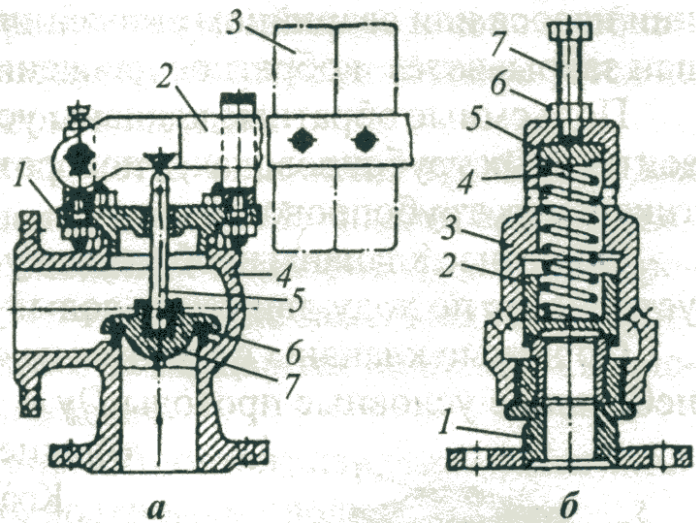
Предохранительные клапаны: а – грузовой клапан: 1 – крышка; 2 – рычаг с грузом; 3 – груз; 4 – корпус; 5 – шпindelь; 6 – седло клапана; 7 – тарелка; б – пружинный клапан: 1 – штуцер; 2 – клапан; 3 – корпус; 4 – пружина; 5 – направляющая втулка; 6 – контргайка; 7 – регулировочный винт
